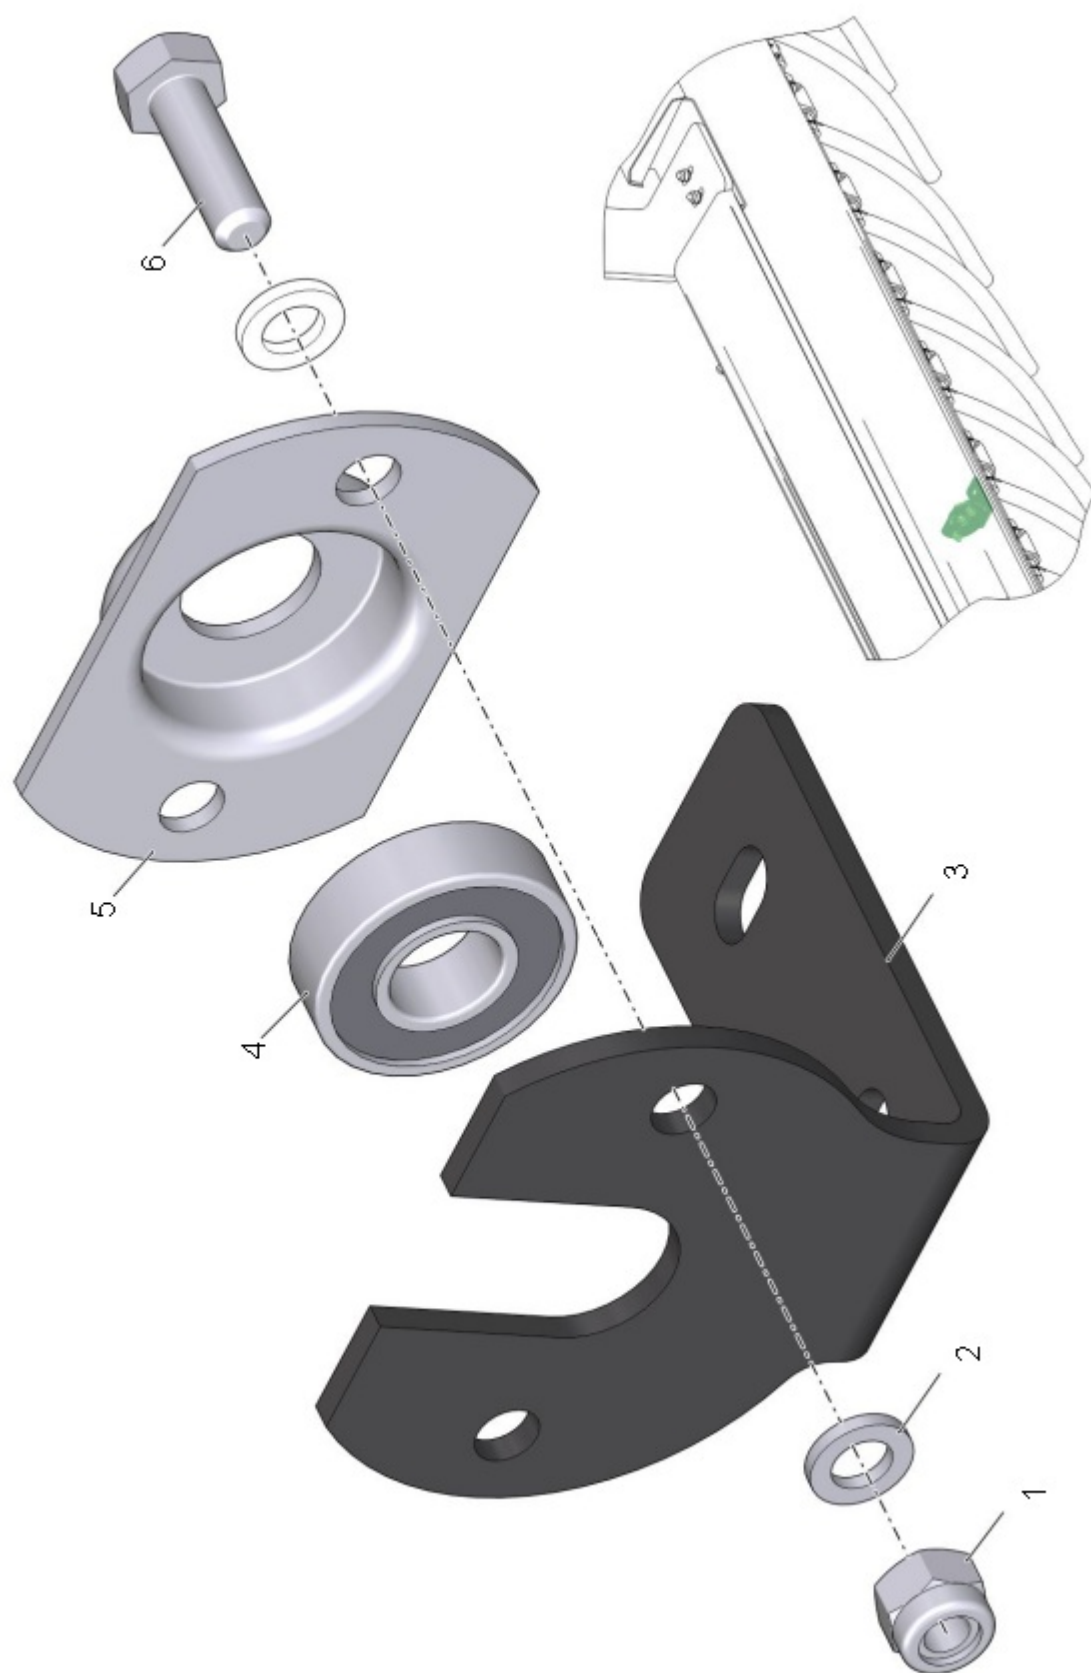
6500.16.90.00А Опора вала ворошилки (Лист 1 из 1)
